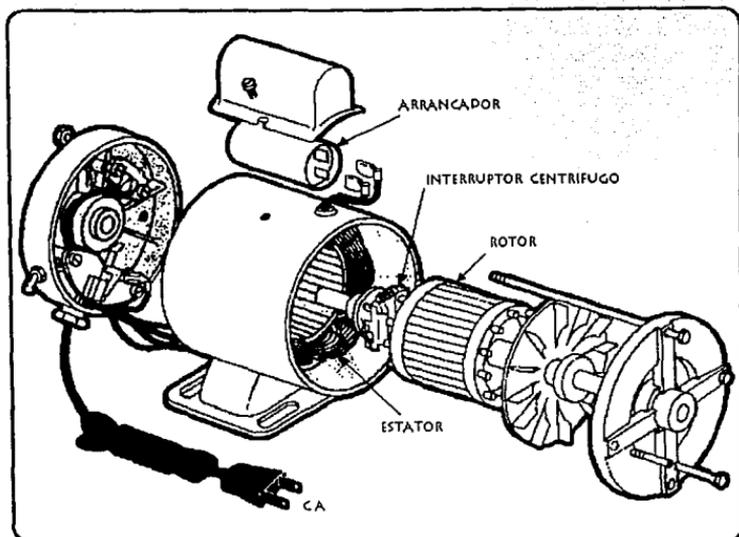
DESPIECE REPRESENTATIVO DE UN MOTOR DE CA MONOFASICO.
